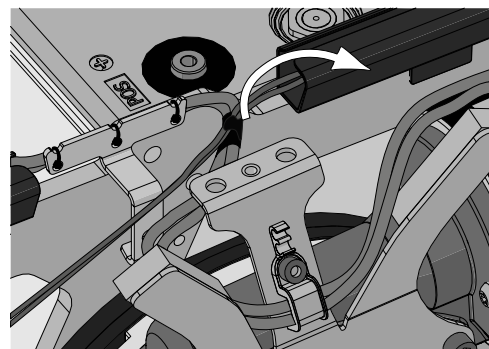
Die Hauptkabel für die vordere Beleuchtung und Blinker sind am Motorkabel befestigt.
